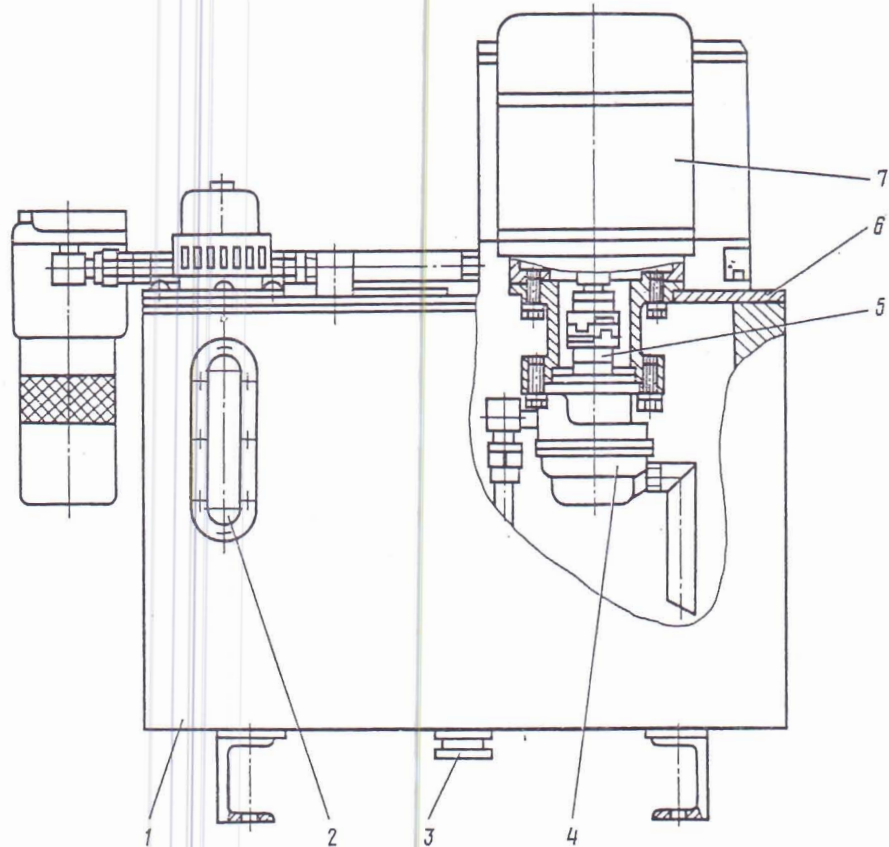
Устройство смазки шлифовальной головки для станка ЗЕ711ВФ1
